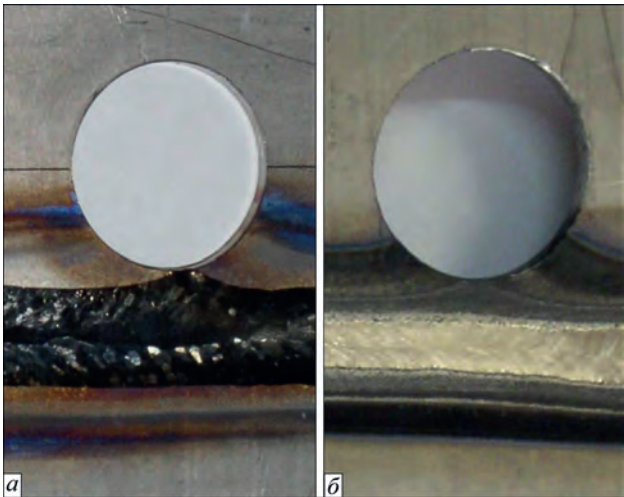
Зовнішній вигляд фрагментів зварних зразків-імітаторів зі сплаву ВТ-20 завтовшки δ = 2 мм при повному проплавленні: а – TIG зварювання, струм зварювання – 100 А; б – A-TIG зварювання, струм зварювання 50 А
